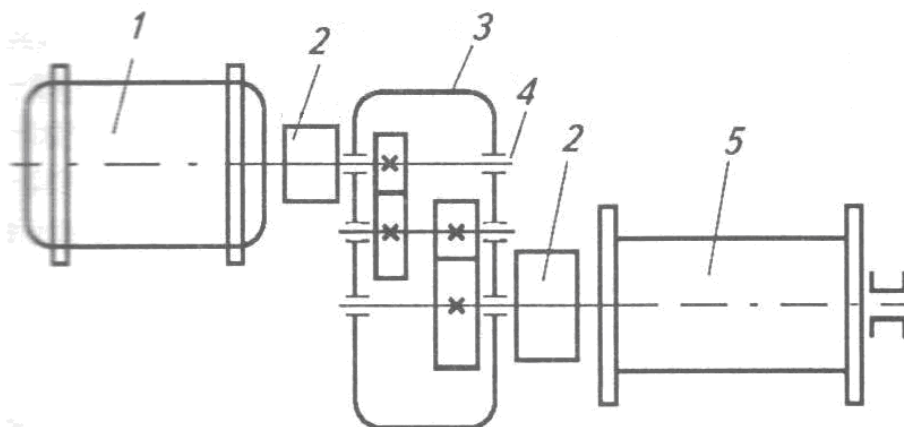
Схема привода грузовой лебедки: 1 – электродвигатель; 2 – муфта; 3 – вал с парой подшипников; 4 – двухступенчатый цилиндрический редуктор; 5 – барабан
